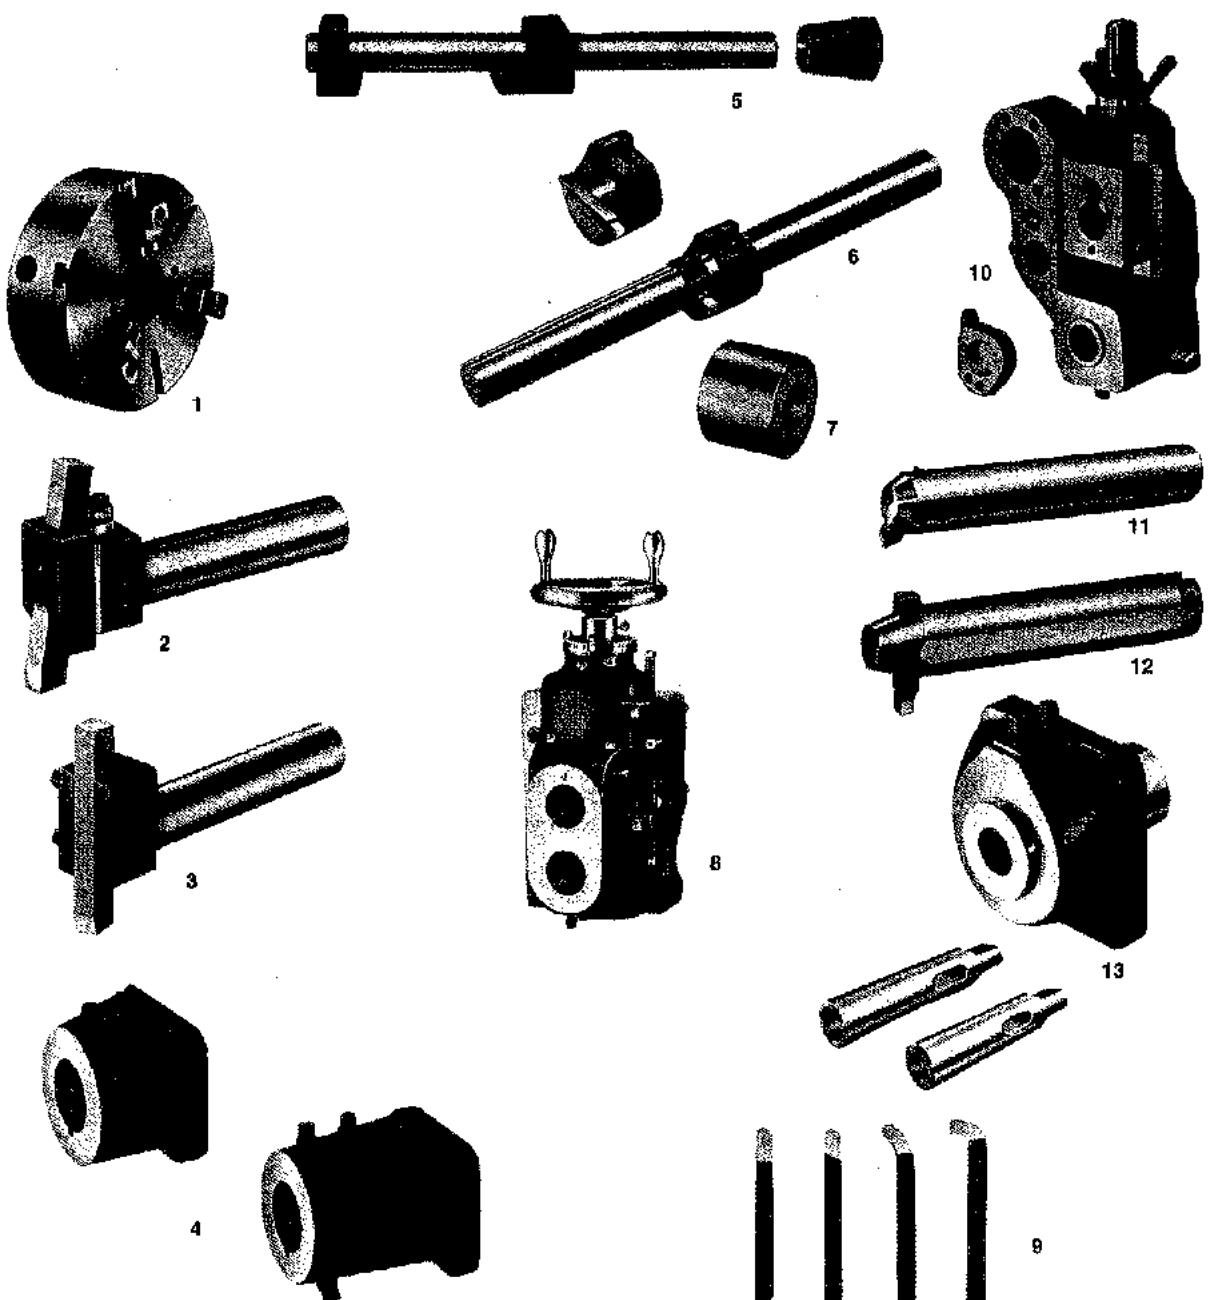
Equipo de herramientas universal para trabajos sobre piezas sujetadas en el plato del torno (Warner & Swasey Co.)
